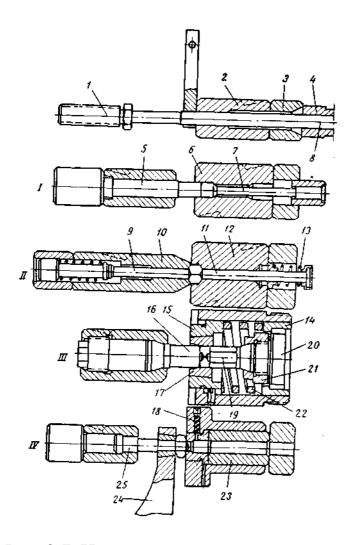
Инструменты для штамповки гайки на позициях I-IV
